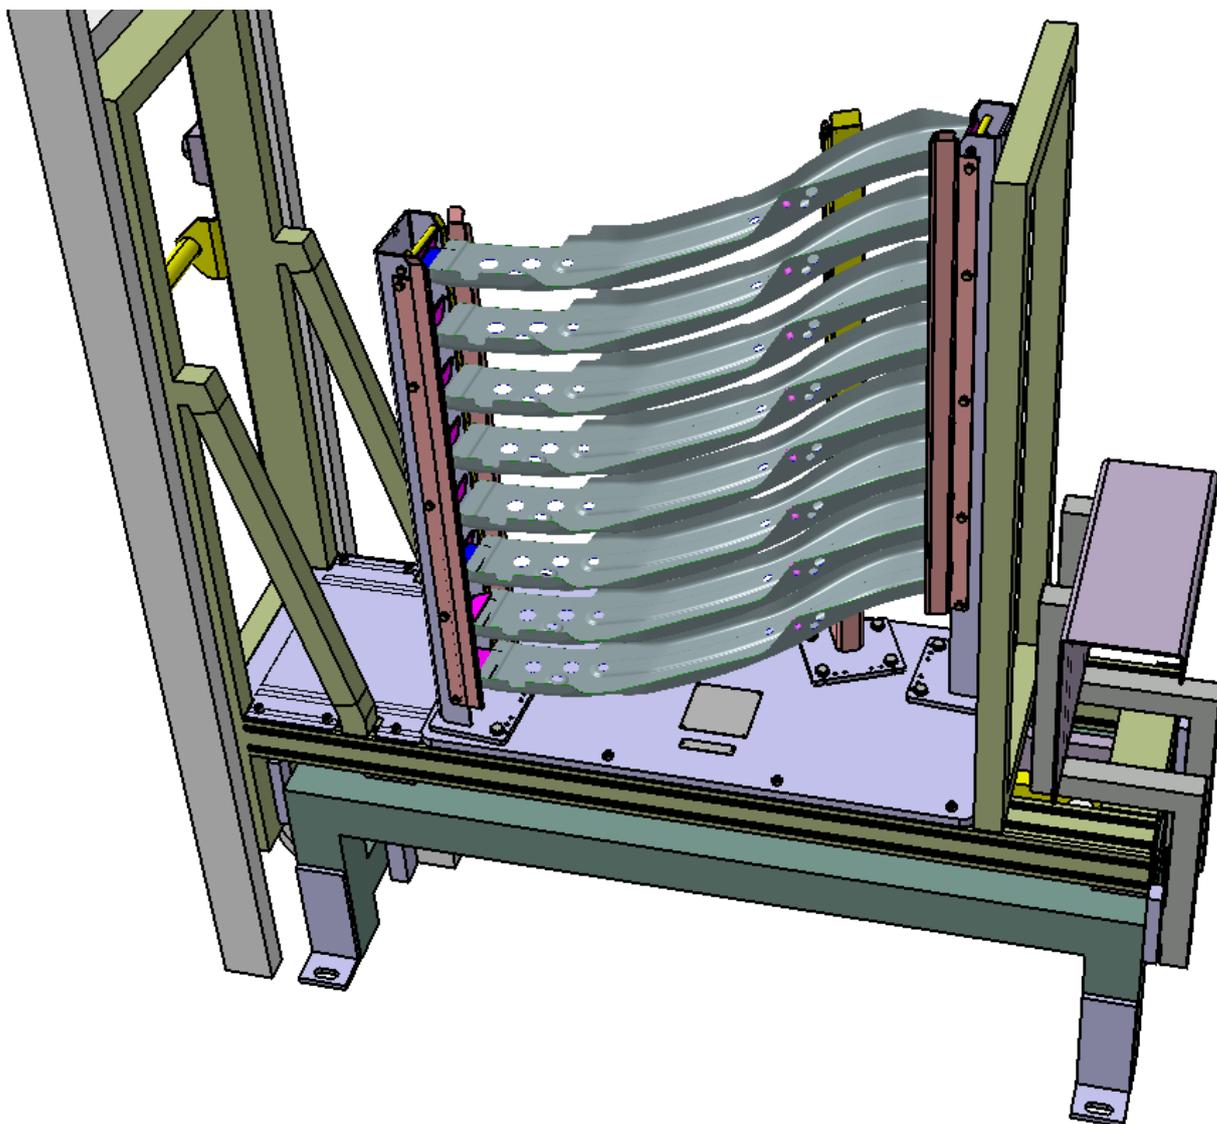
Тележка для передачи деталей на сборочный участок
